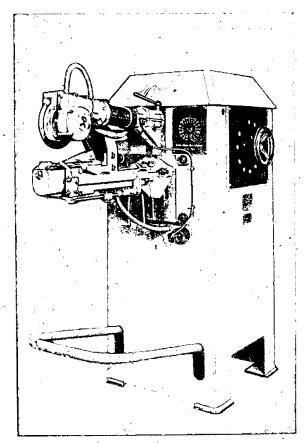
Stumpf-Schweißmaschine (Peco)
